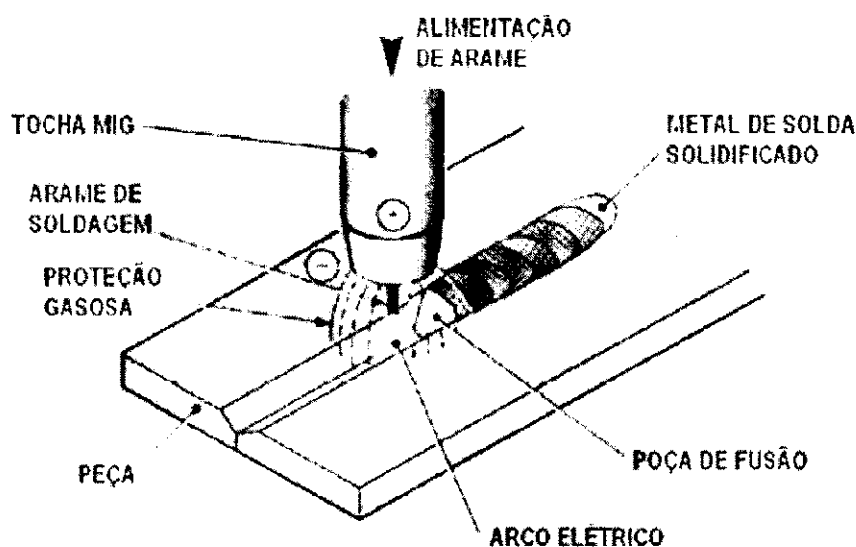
Processo básico de soldagem MIG/MAG. Fonte: Fortes (2007)
